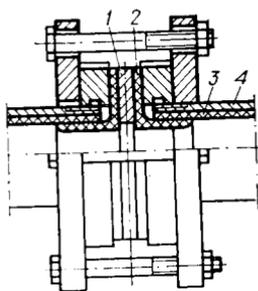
Фланцевое соединение с вклеенной пластмассовой втулкой: 1 — прокладка; 2 — пластмассовая втулка; 3 — футерующий слой; 4 — металлическая труба.
